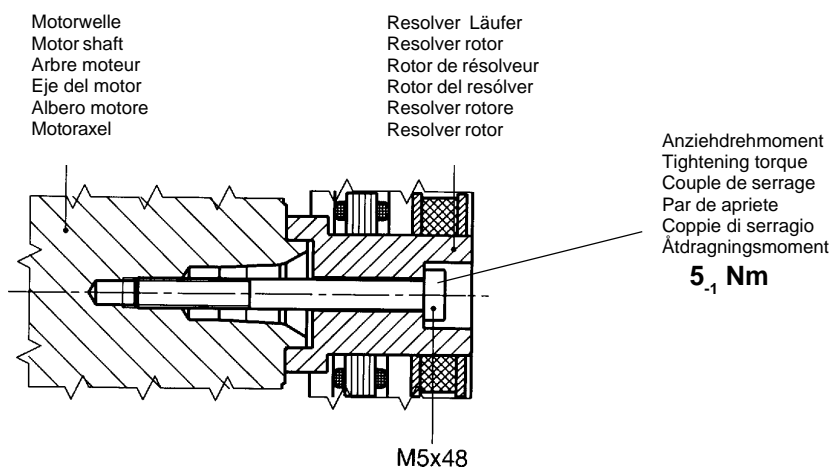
Verbindung Motorwelle - Resolver Läufer / Joint between motor shaft and resolver rotor
